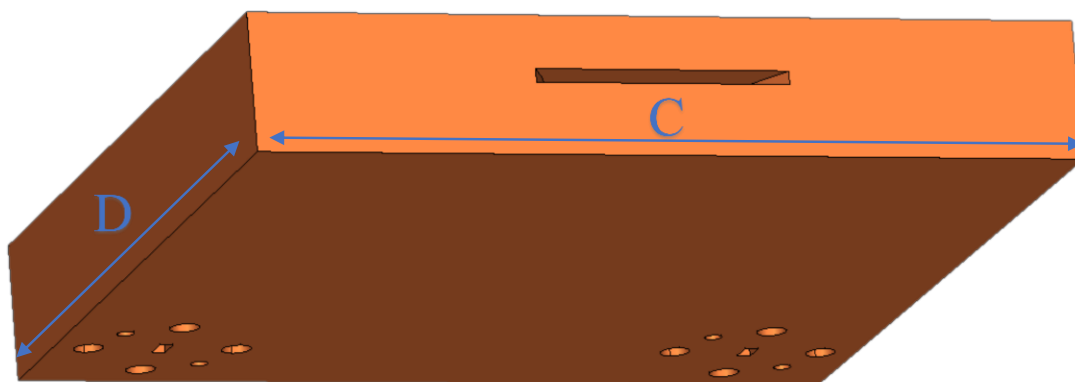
bloque del dispositivo a fabricar mediante la técnica *diffusion bonding*. Vista en perspectiva.
